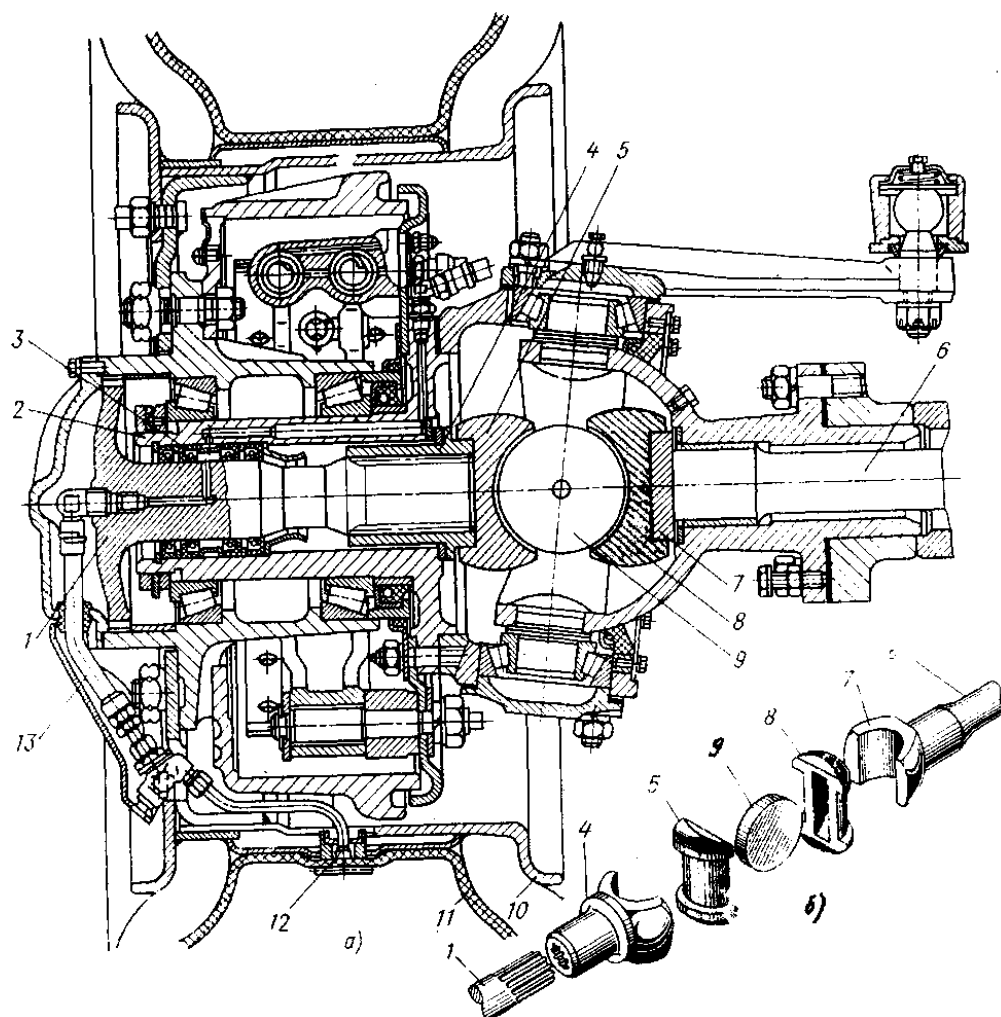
Привод переднего колеса автомобиля «Урал - 375»: а – общий вид привода; б – детали кулачкового карданного шарнира; 1 – наружная полуось; 2 – поворотная цапфа; 3 – уплотнительные манжеты; 4 и 7 – вилки; 5 и 8 – кулаки; 6 – внутренняя полуось; 9 – диск; 10 – обод колеса; 11 – шина; 12 – соединительная муфта; 13 - трубопровод
